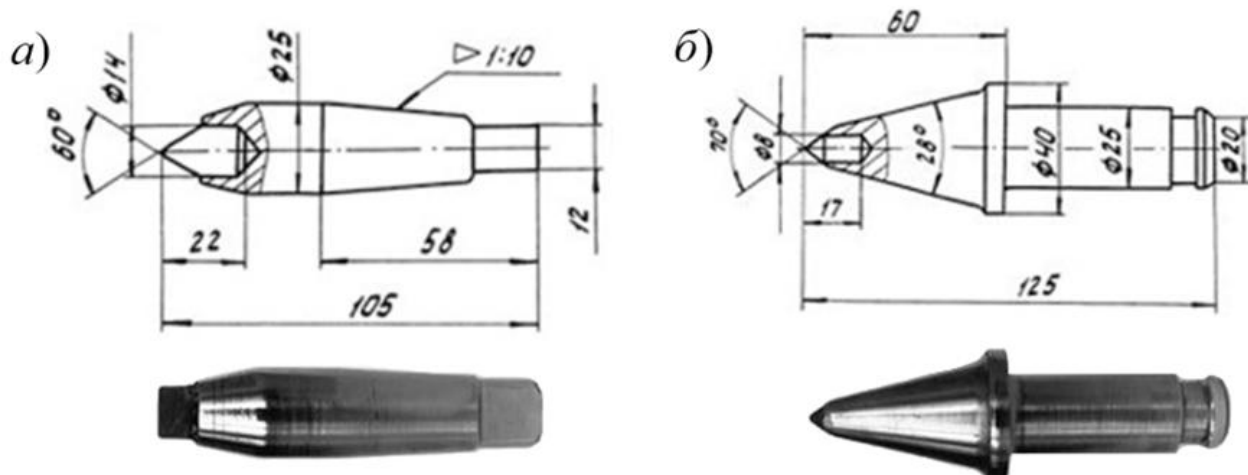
Резцы комбайнов для добычи калийной руды:
